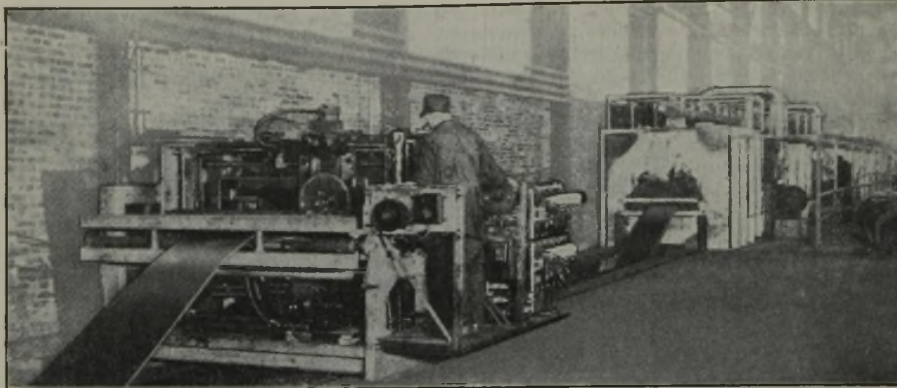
Punktschweißmaschine für das Aneinanderschweißen der Blechstreifen.
